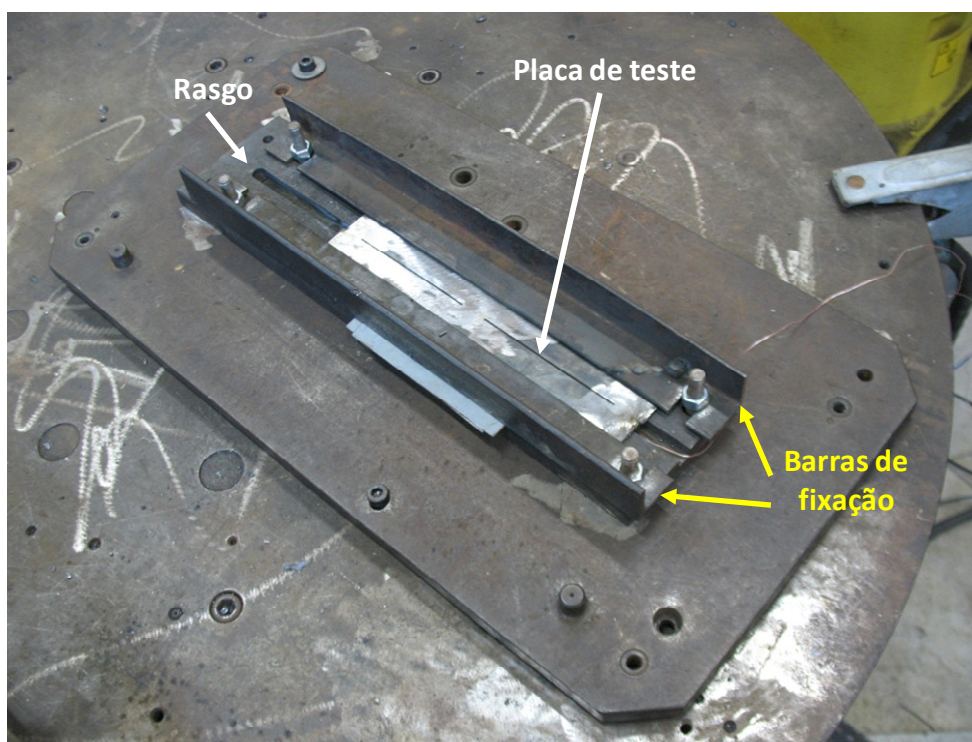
Suporte para fixação das placas preparadas para os testes com juntas (atentar para o rasgo no suporte, que tem como objetivo simular soldagem sem sobreposição) - dimensões: 100 x 420 mm
